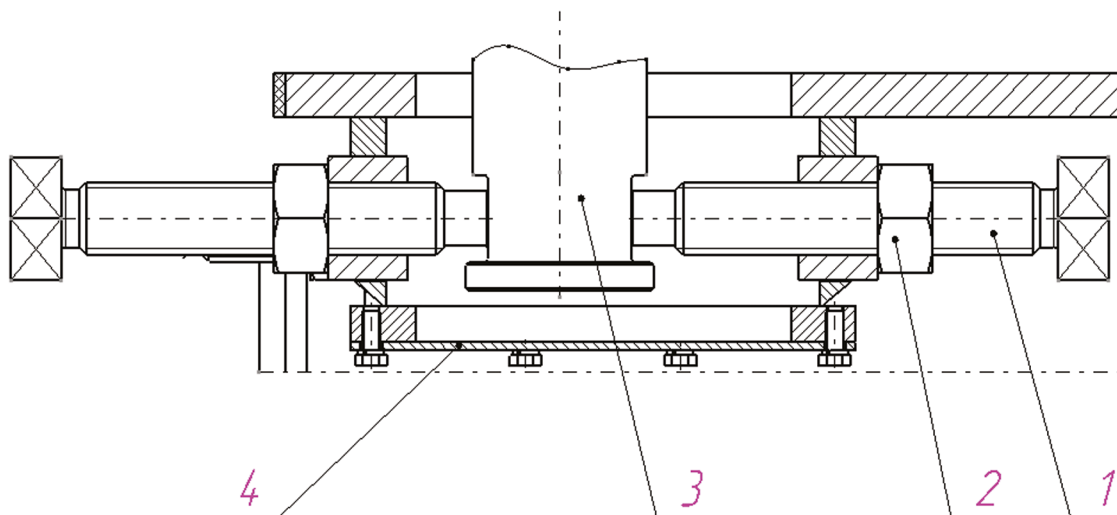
Механизм регулировки положения отбойной плиты и решетки колосниковой относительно ротора
